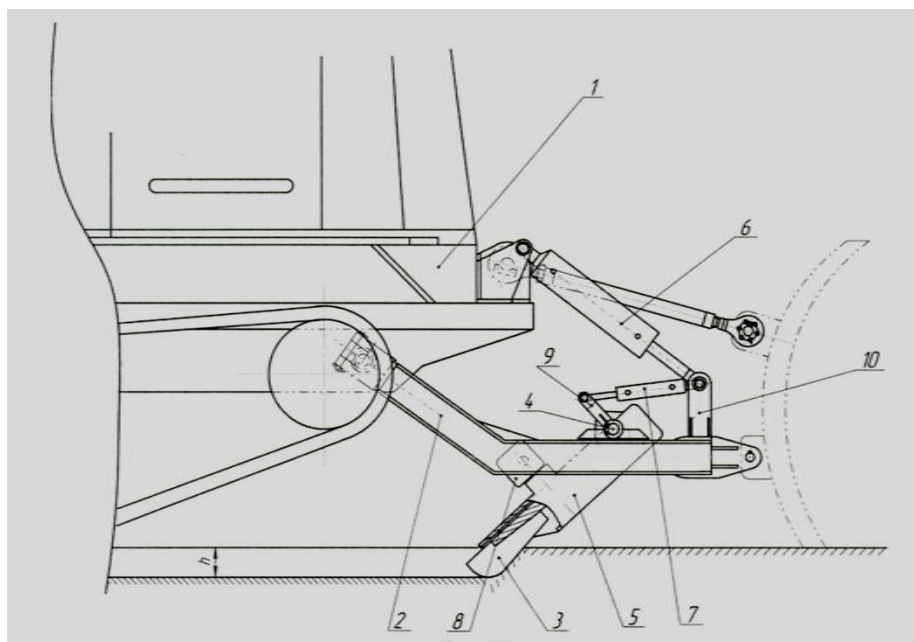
Общий вид фронтального лесопожарного грунтомета
